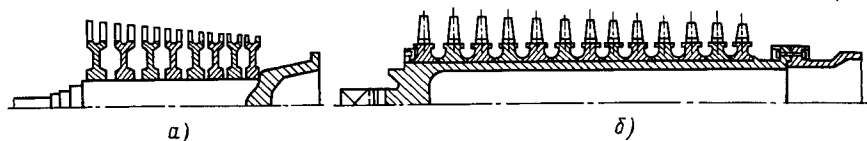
Роторы с насадными дисками осевых компрессоров ГТУ фирмы Вестингауз:
